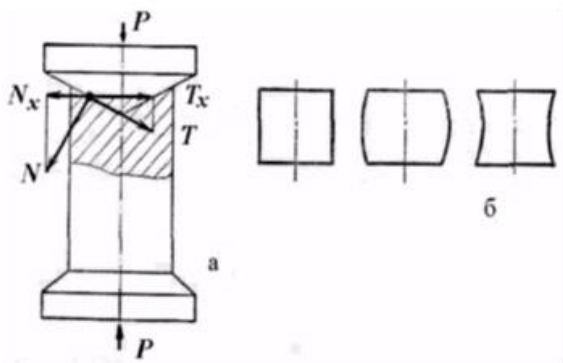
Осадка заготовок: *a* – коническими плитами; *б* – форма боковой поверхности образцов [13]
